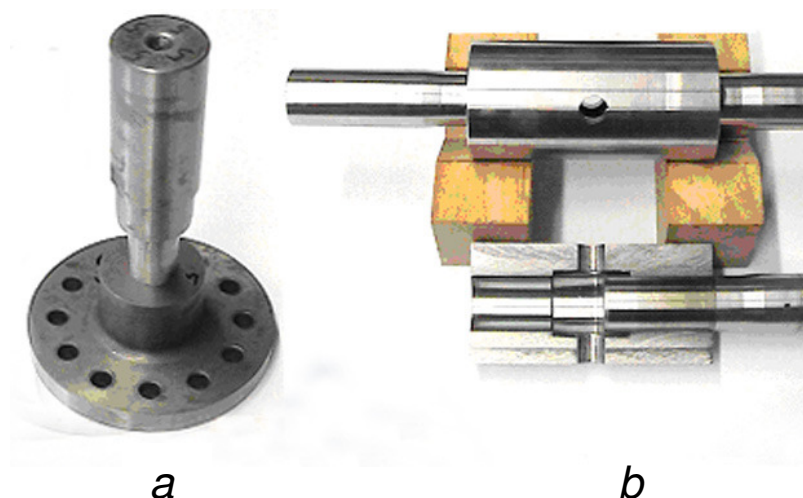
Probenformen, *a* Probe mit Flanschnabe, *b* IKTD
